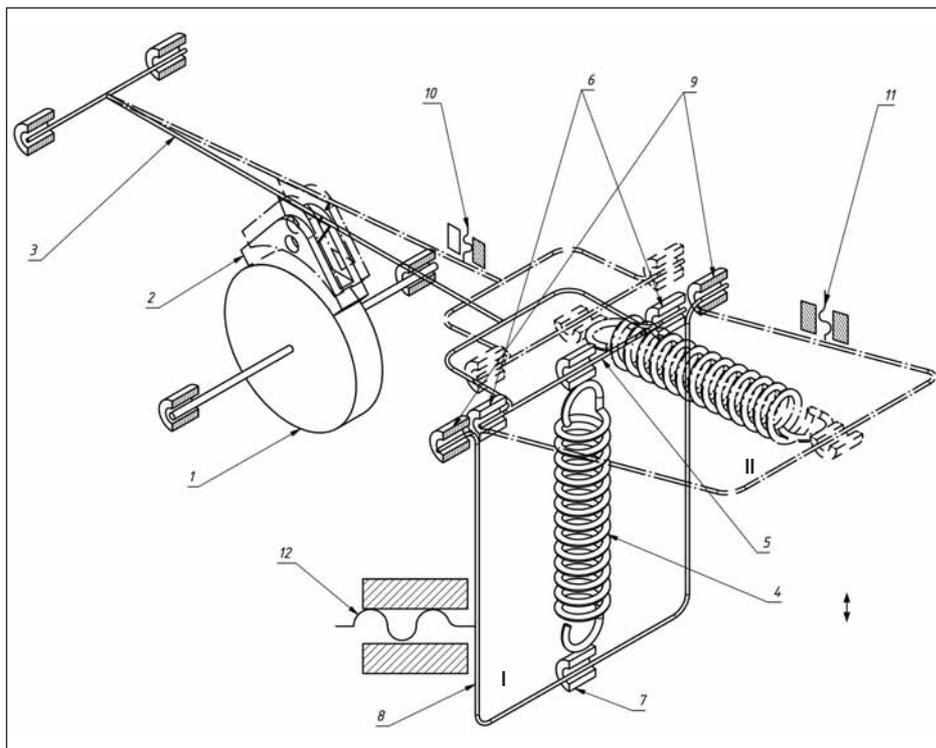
Конструктивная схема простейшего колодочного тормоза с поворотной пружиной
